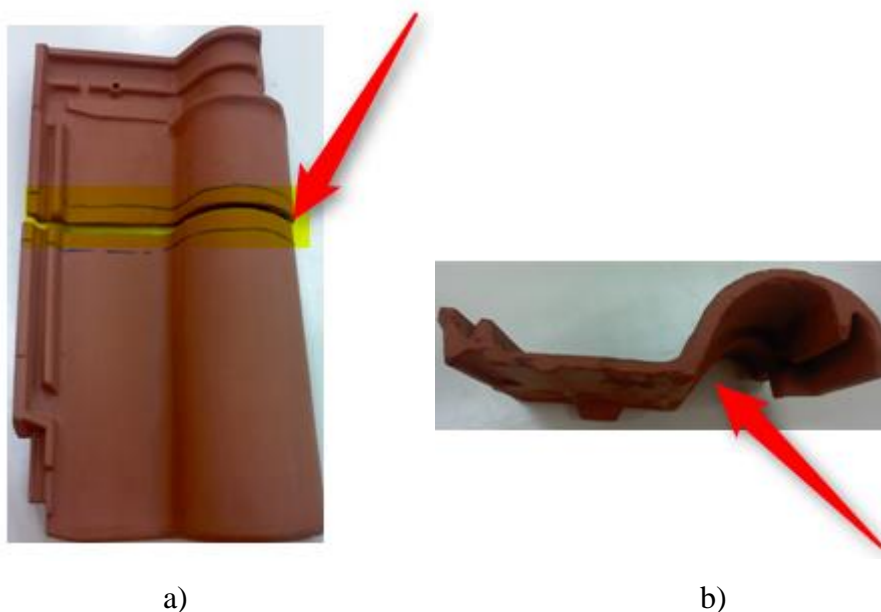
Zona de corte da telha a) e respetivo perfil em b).
